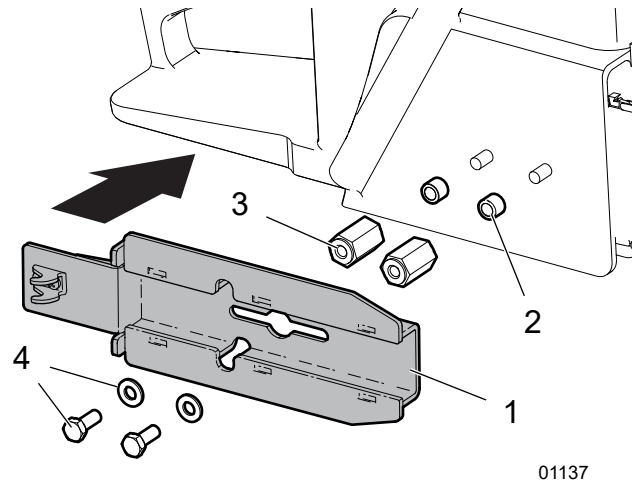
Installation de l'adaptateur universel pour scie à chaîne
